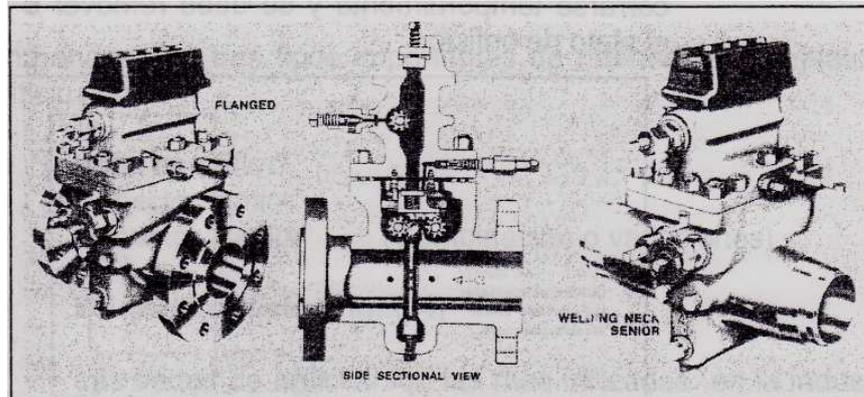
Modelo de Conector Senior, de Brida y de Soldar (Daniel Industries; Inc)
